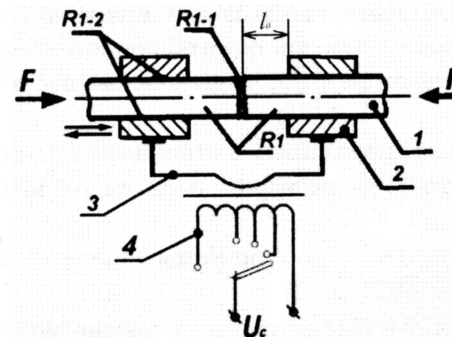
Схема контактной-стыковой сварки: 1 — свариваемые заготовки; 2 — электроды; 3 — вторичная обмотка трансформатора; 4 — первичная обмотка трансформатора
